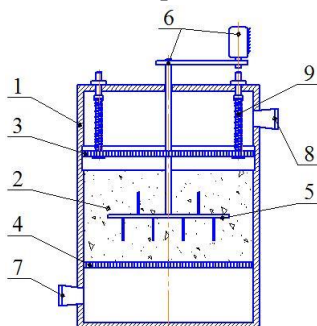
Адсорбер для зневоднення етанолу: 1 – корпус; 2 – сорбуючий шар(адсорбент); 3, 4 – обмежувальні решітки; 5 – розпушувач сорбенту; 6 – привід розпушувача; 7, 8 – патрубки; 9 – притиски
